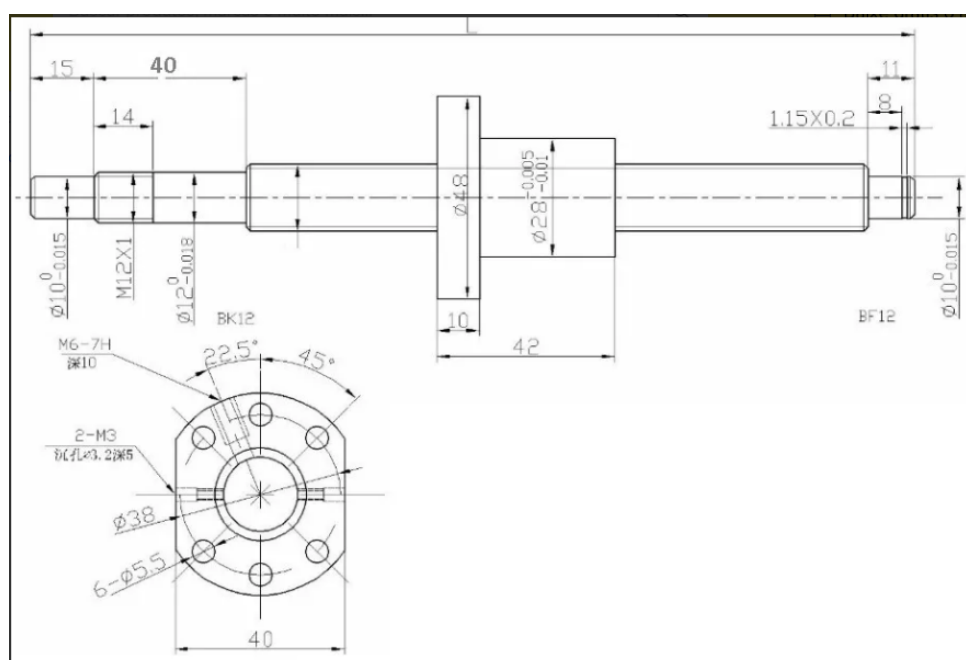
Desenho de usinagem para padrões BK12, BF12, FK12 e FF12.
